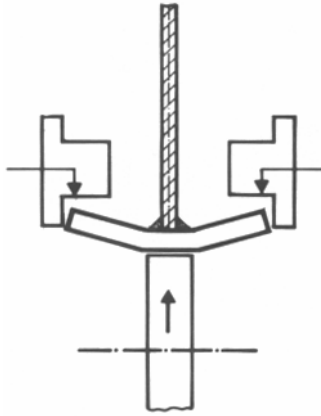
Operación de postdeformación tras la soldadura en un ensamblado.
